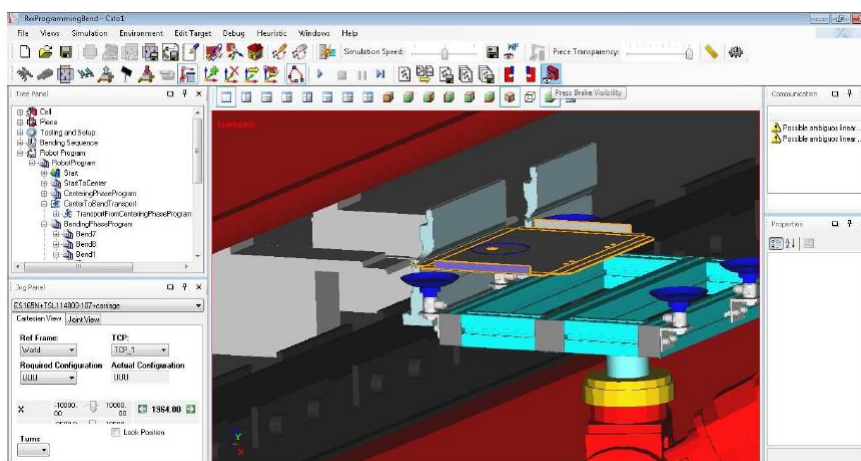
Definição do processo de quinagem com o RoboWave Bending
